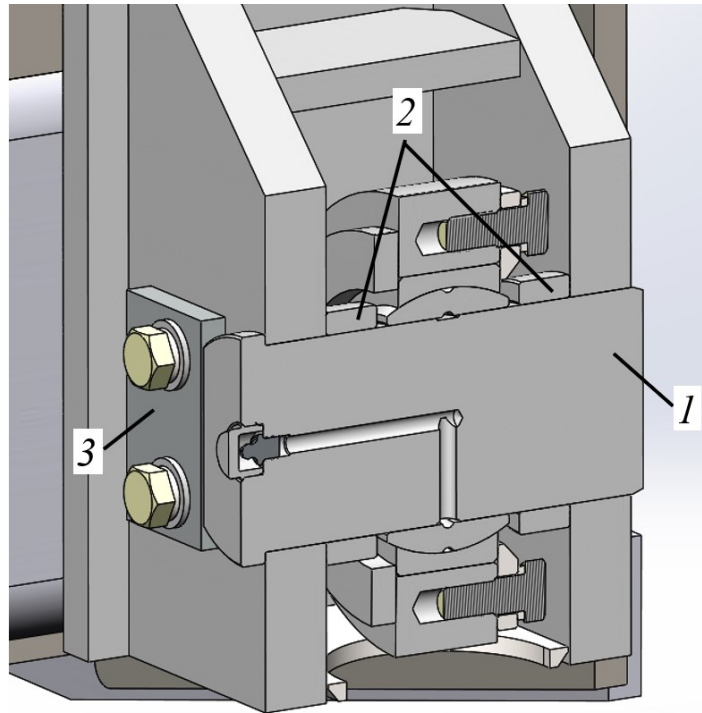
Установка пальца крепления зеркала отвала к брусу
